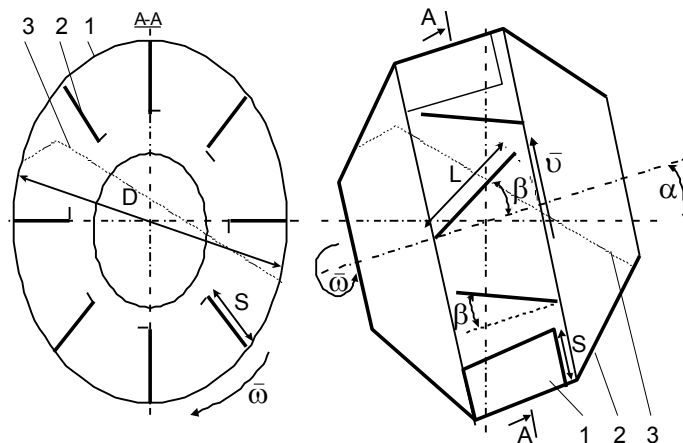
Схема перемешивающего аппарата барабанного смесителя:
